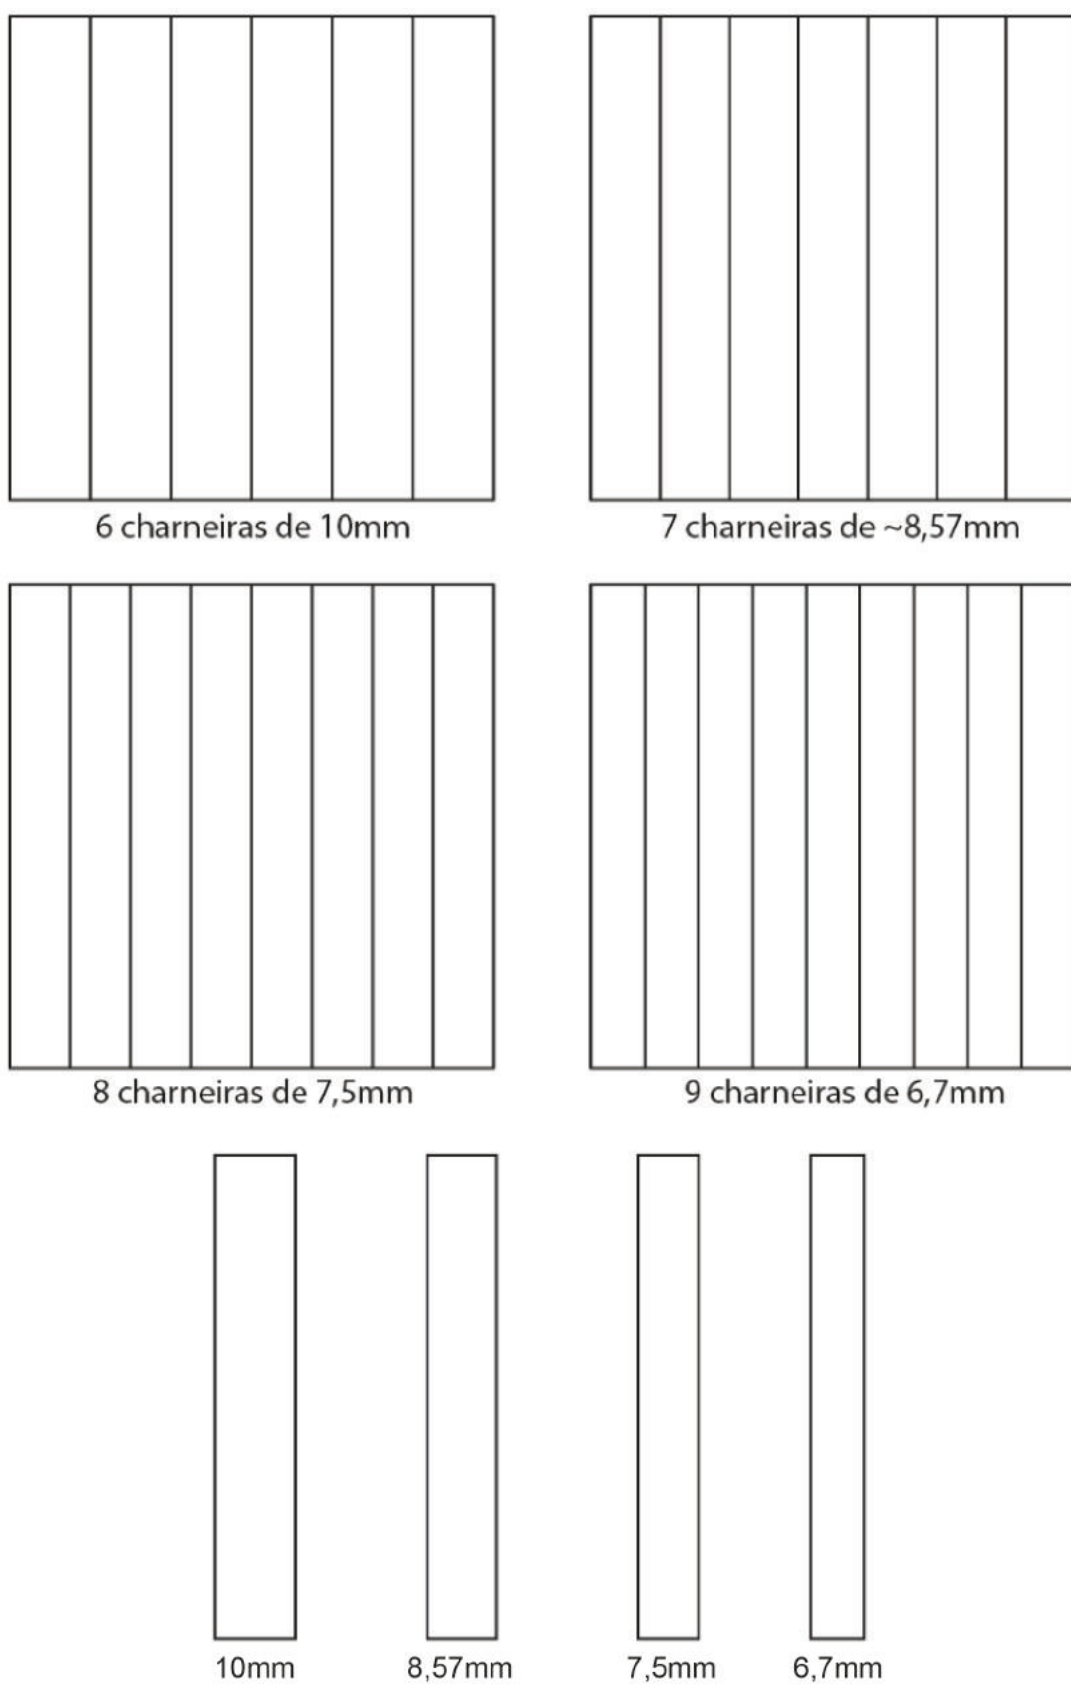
Esquema de diâmetros das charneiras tamanho 1:1. Fonte: Acervo da autora.
